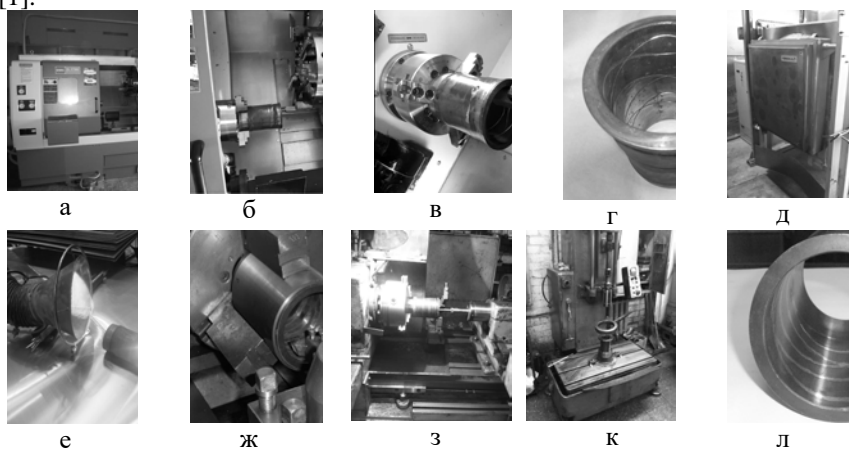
Металлизированная гильза цилиндров: а) общий вид токарного обрабатывающего центра DMC серии Т модель DL6TMH; б) трёхкулачковый патрон; в) резец ВК8; г) гильза цилиндров с нарезанными синусоидальными и эллиптическими канавками; д) общий вид электропечи «Накал»; е) наплавка канавок медью М1; ж) зачистка внутренней поверхности; з) операция шлифование; к) процесс хонингования; л) металлизированная гильза цилиндров
